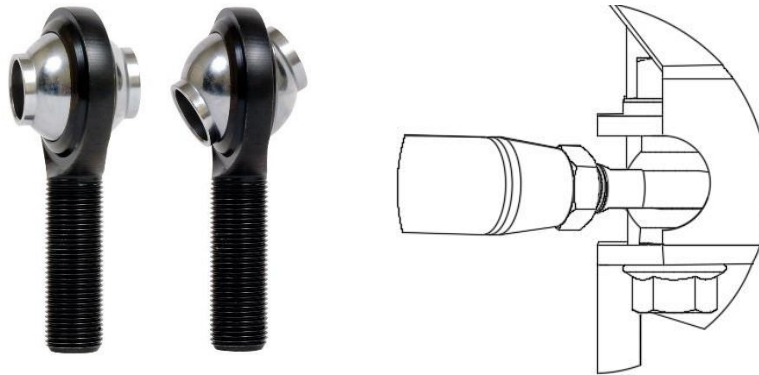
Rotula utilizada en el ensamble al soporte al bocín.
